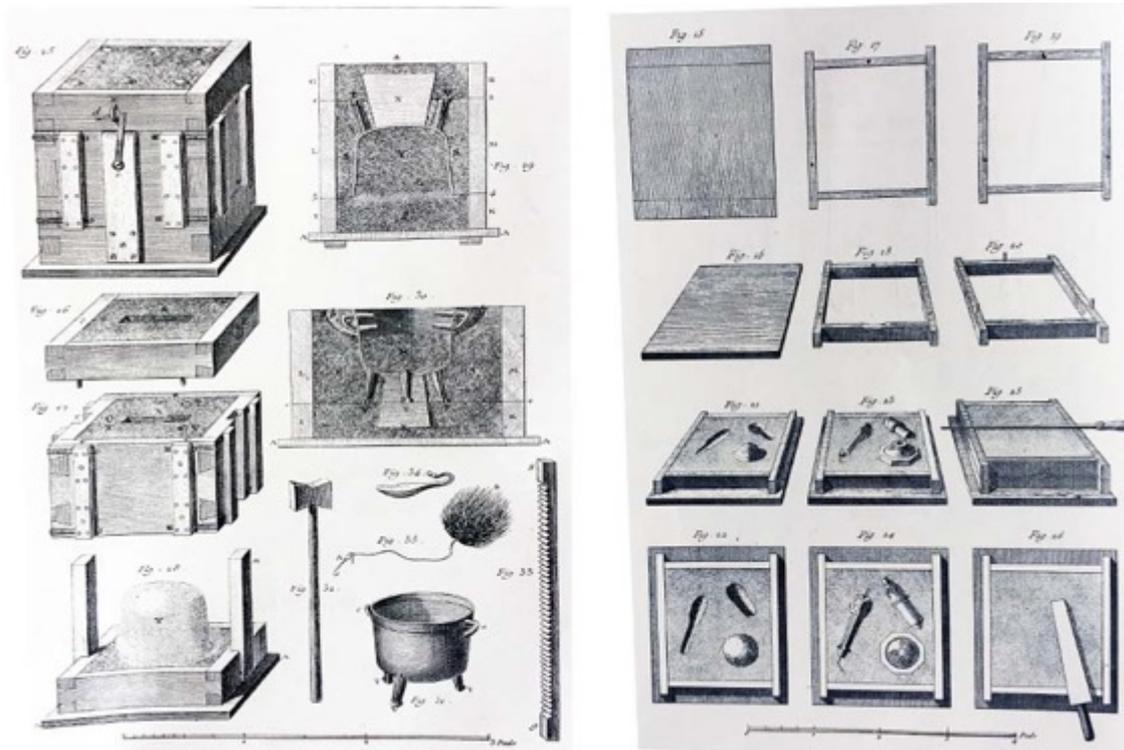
333- 339. XVIII<sup>e</sup> siècle. Moulage en châssis et petit outillage de l'ouvrier démouleur et moulage d'un chandelier.
